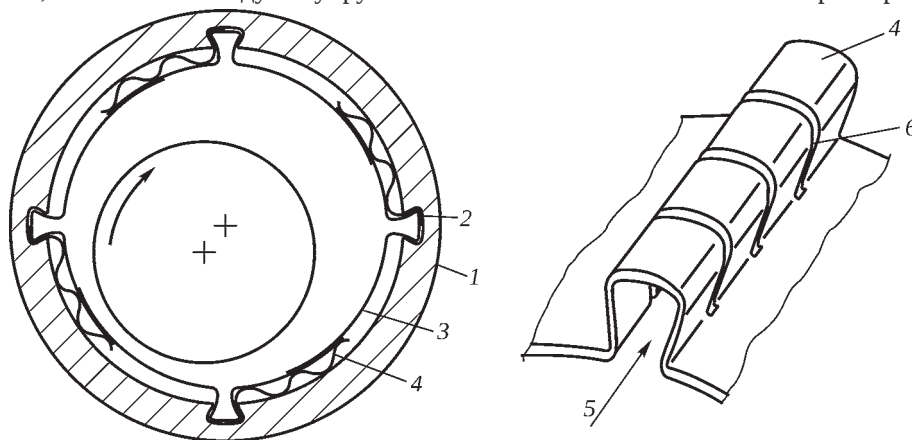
Схема дополнительного охлаждения подшипника [20]: 1 – обойма; 2 – канавка; 3 – гладкий лепесток; 4 – гофрированный элемент; 5 – охлаждающий поток; 6 – дополнительные прорезы
